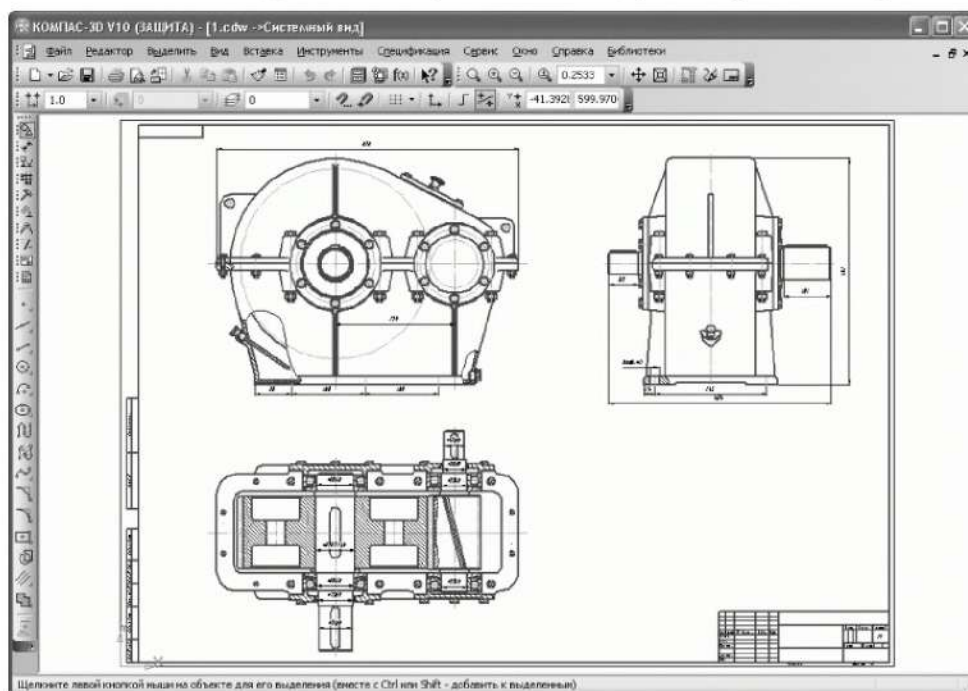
Чертеж цилиндрического редуктора, сгенерированный прикладной библиотекой Редуктор-2D V1.7
